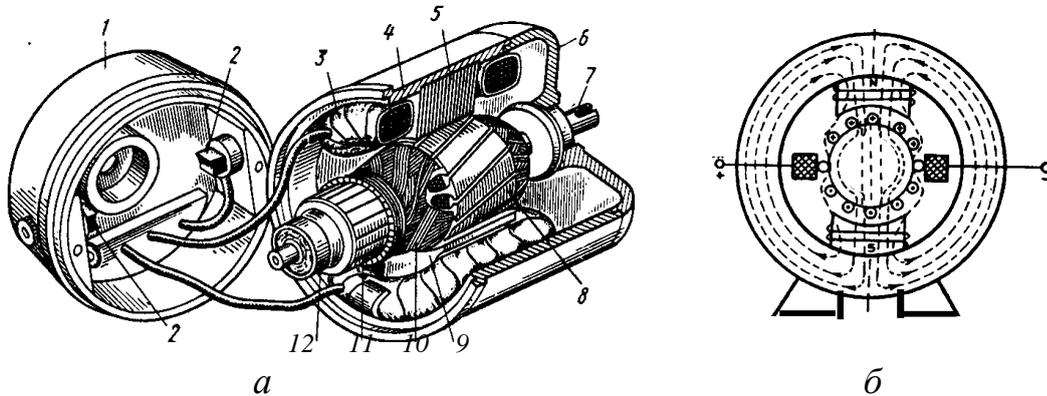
Внешний вид конструкции и схематическое устройство двигателя постоянного тока
